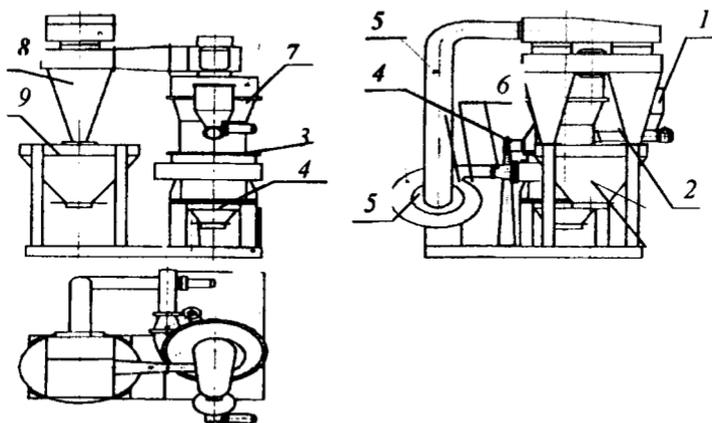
Лабораторный измельчительный комплекс: 1 – приемный бункер; 2 – шнековый питатель; 3 – мельница; 4 – бункер для металлической фракции; 5 – вентилятор; 6 – шибер для регулировки давления воздуха; 7 – классификатор; 8 – осадительный циклон; 9 – бункер для дисперсной фракции
